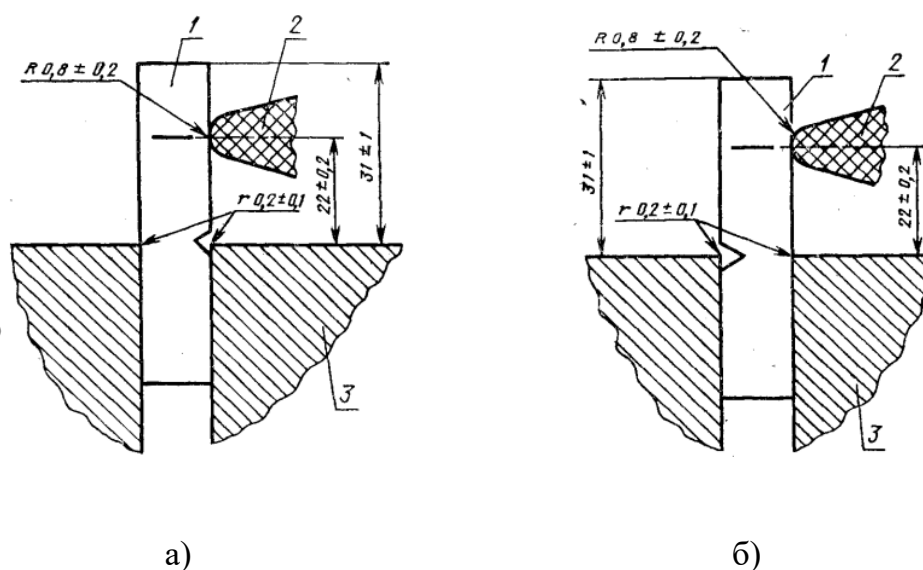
Схема закрепления образца: а – надрезанный образец; б – ненадрезанный образец; 1 – образец; 2 – маятник; 3 – зажим
